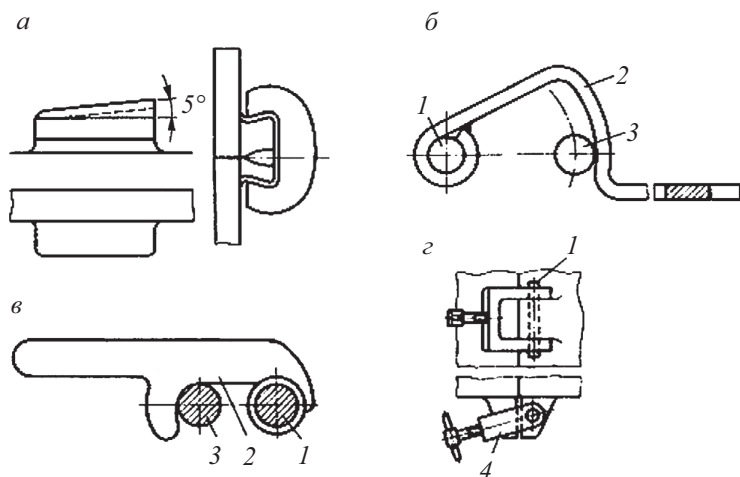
Запорные устройства для скрепления частей кокиля:
